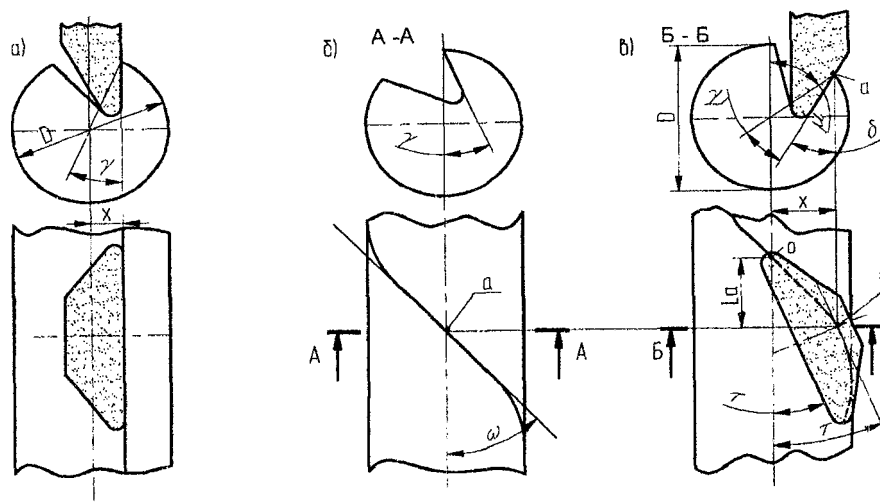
Схемы заточки передних поверхностей зубьев с режущими кромками на цилиндрической поверхности фрезы.
